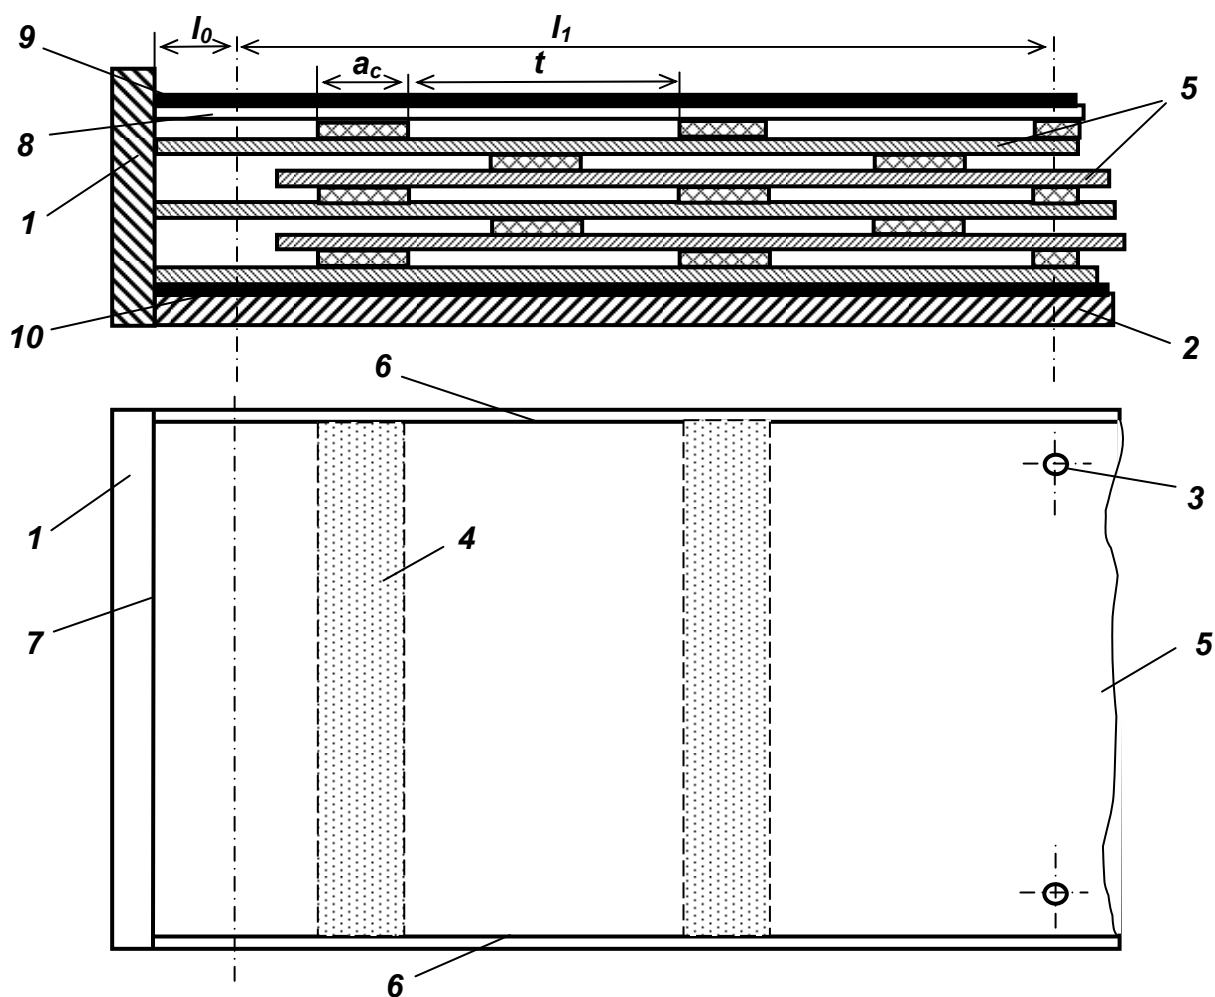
Схема сборки сотопакета в фиксирующем приспособлении:
